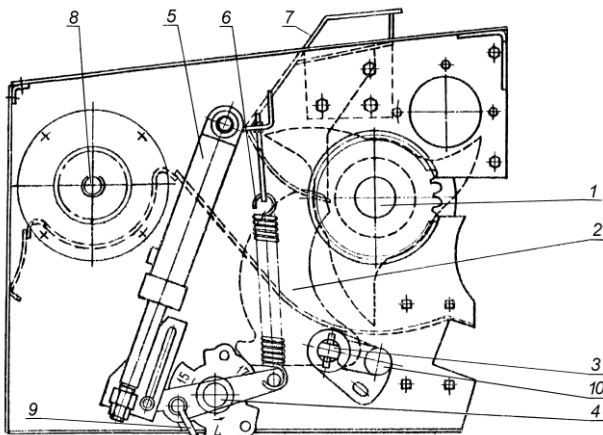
Измельчитель: 1 – подающий барабан; 2 – нож; 3 – ось ножей; 4 – вал; 5 – гидроцилиндр; 6 – пружина; 7 – гребенка; 8 – нижний передний валец; 9 – рычаг; 10 – фиксатор оси ножей.
